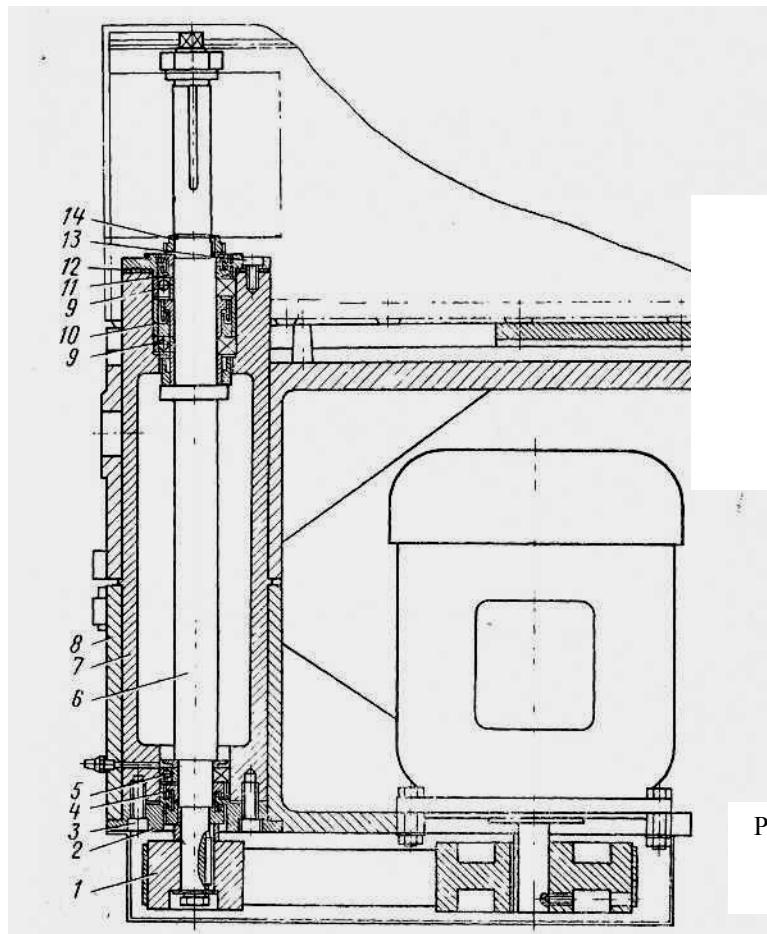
Вертикальный суппорт четырехстороннего продольно-фрезерного станка С25-01
